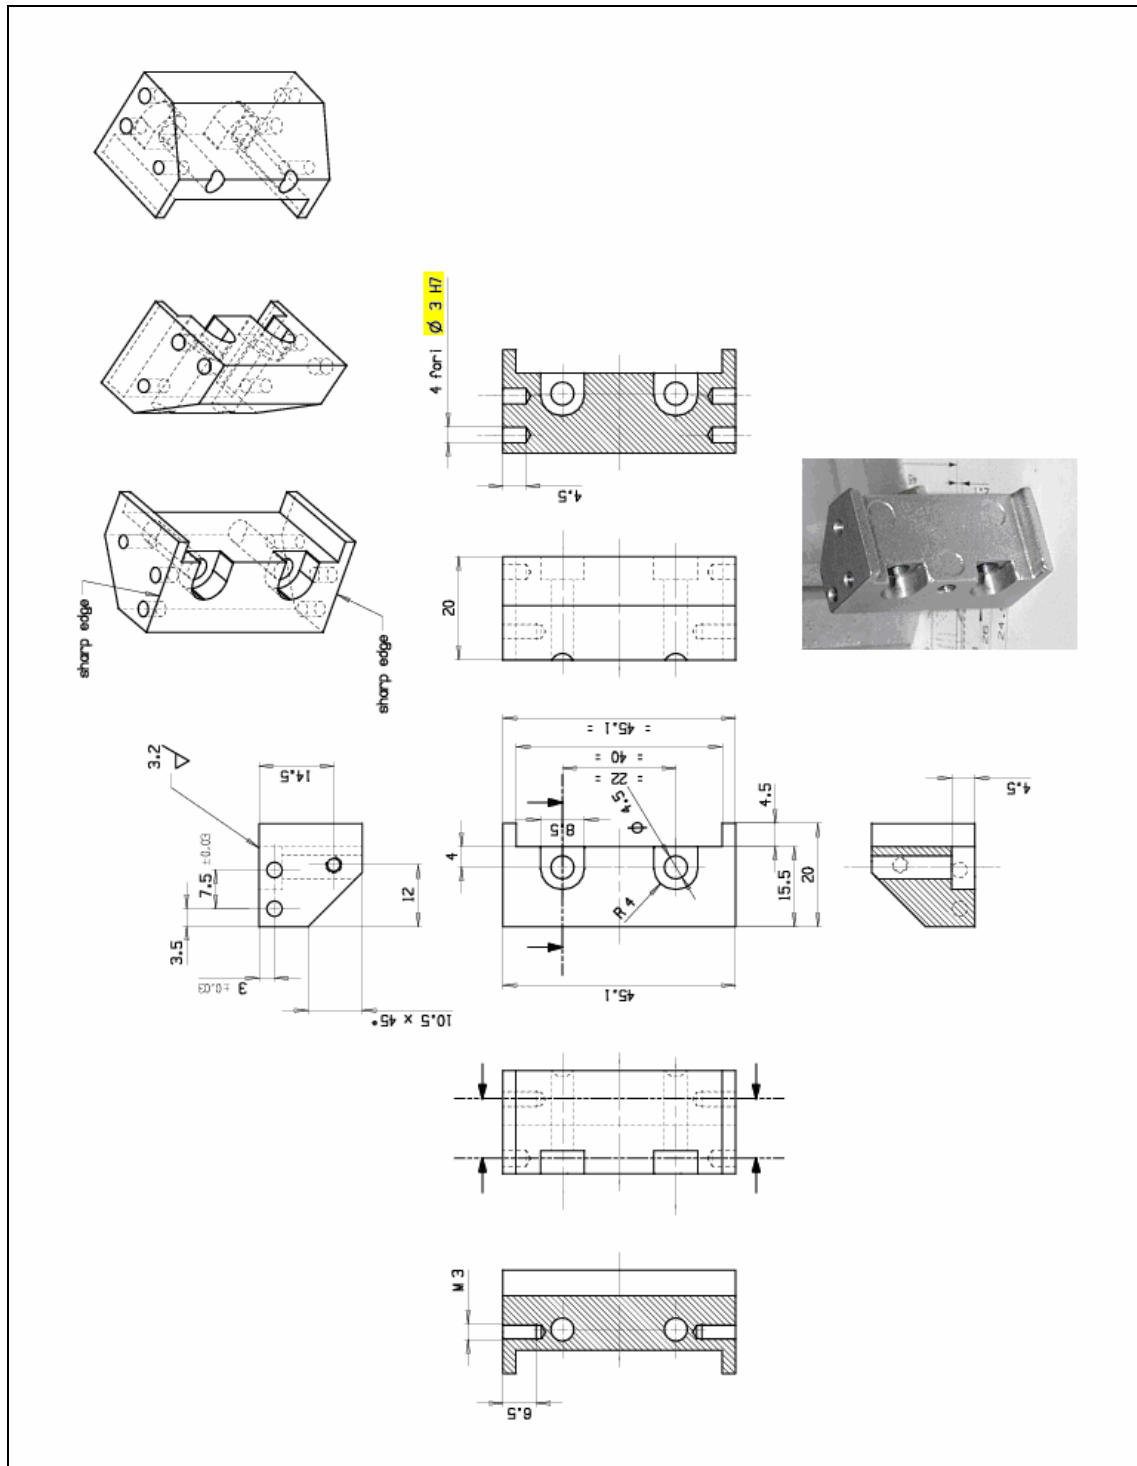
Plano de fabricación de las piezas verticales de aluminio (column)
